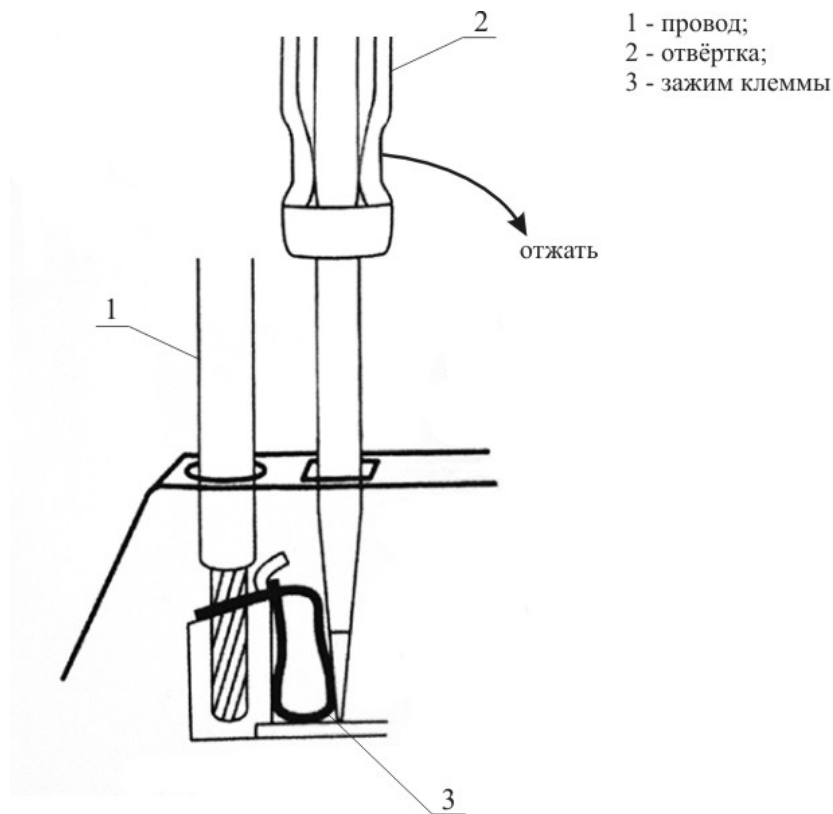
Крепление провода пружинным механизмом клемм
